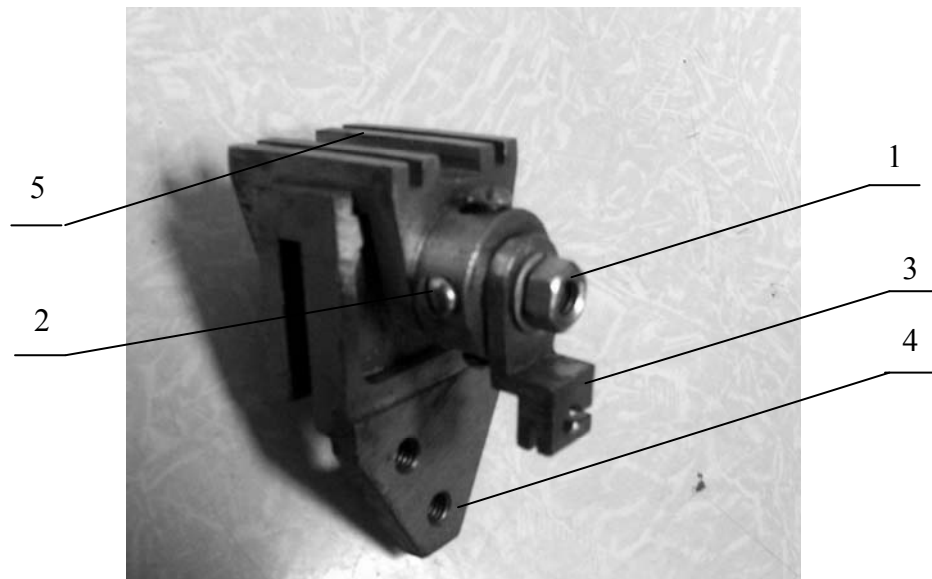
Экспериментальный образец дискового тормоза с механическим приводом: 1 – гайка; 2 – механическое нажимное устройство; 3 – рычаг; 4 – корпус; 5 – скоба
